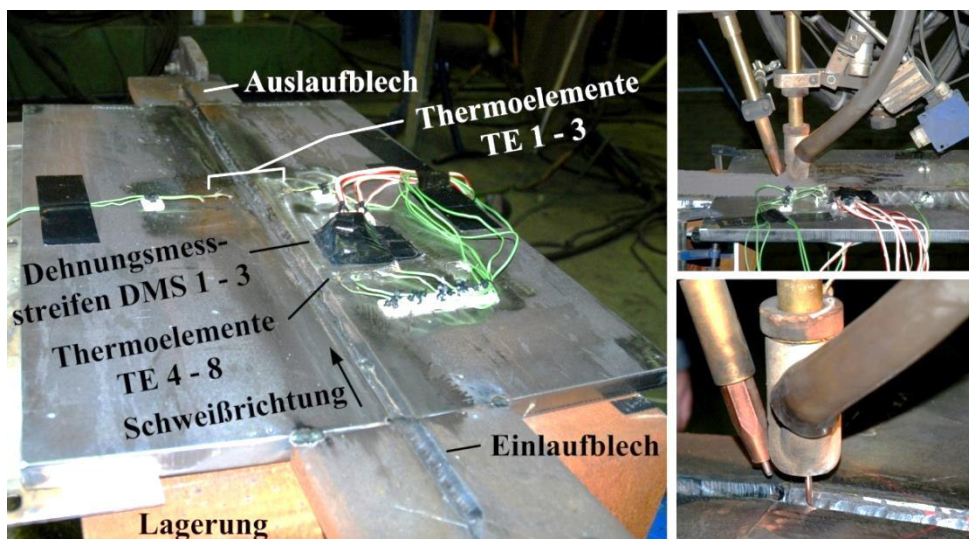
UP-Schweißen beim Turmhersteller, Schweißstand mit Probe und Messtechnik
